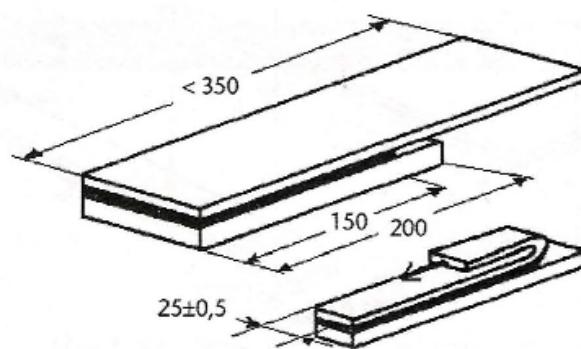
Geometria de ensaio de arrancamento a 180° (dimensões em mm).
